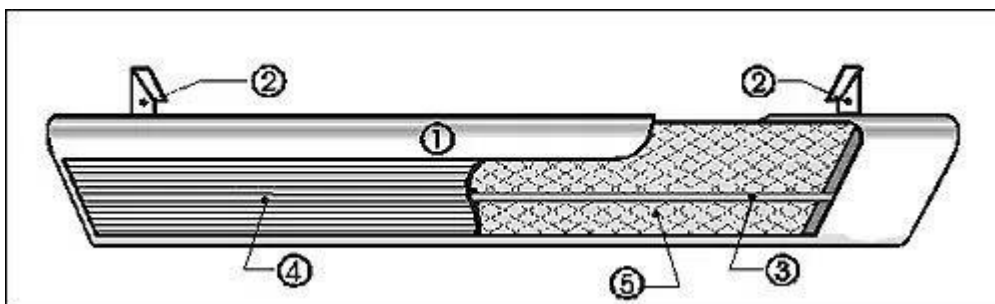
Устройство потолочного обогревателя: 1 – металлический корпус; 2 – кронштейны крепления к потолку; 3 – ТЭН; 4 – излучающая пластина из алюминия; 5 – слой тепловой изоляции с отражателем
